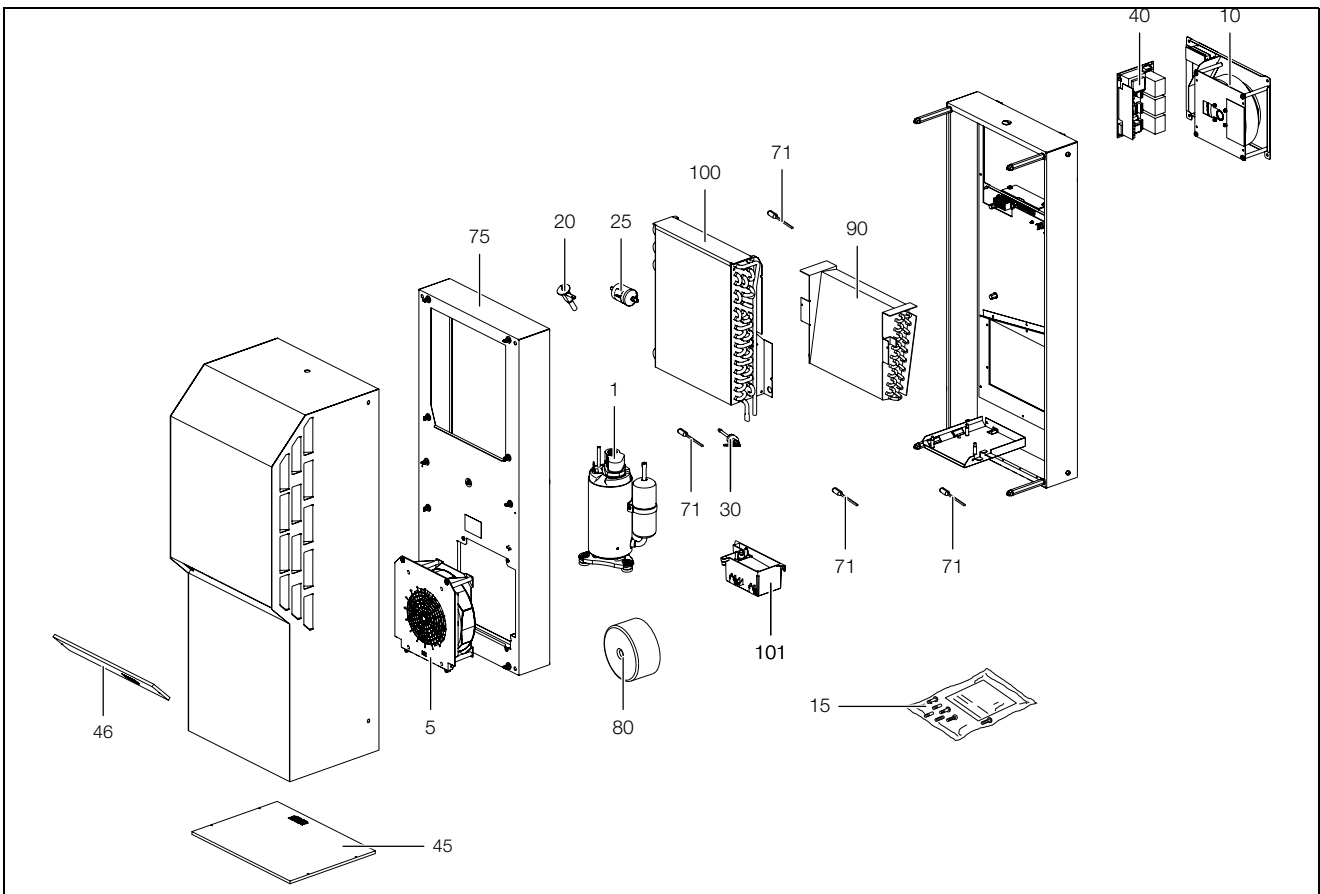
pièces de rechange 3304.5x8, 3305.5x8
